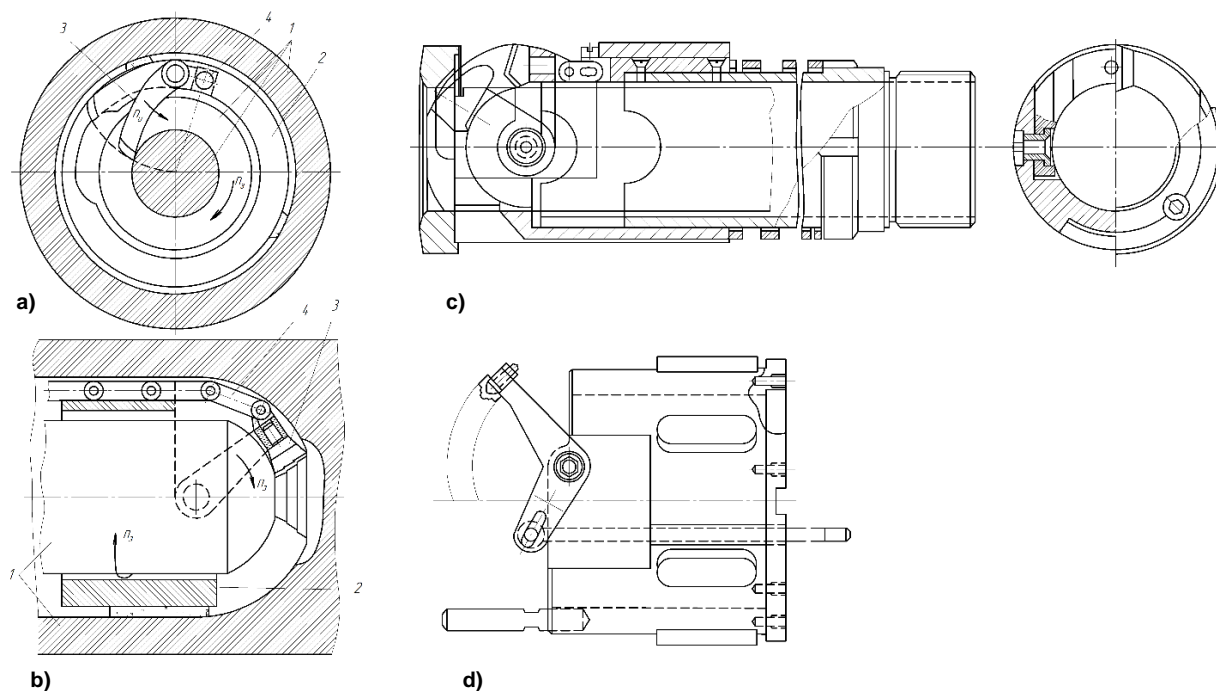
Специализированные инструменты для отделения стержня, образующегося при высверливании, классифицируются следующим образом: а) устройства с резцом, совершающим движение в направлении, перпендикулярном оси заготовки; б) устройства, в которых резец перемещается в плоскости, параллельной оси заготовки; в) головка для разделения сердечника, оснащённая шарнирным механизмом и дуговым держателем режущего инструмента; д) головка для отрезки сердечника с дуговым резцедержателем.
